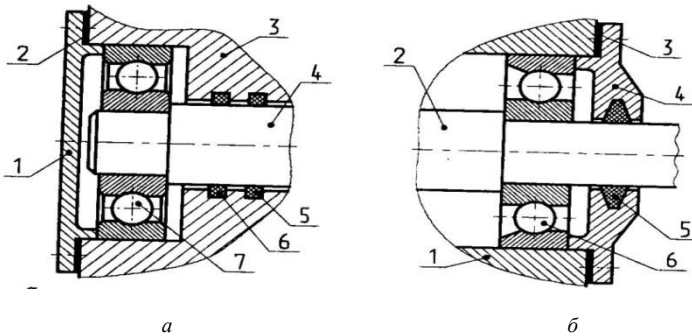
Уплотнители: а – уплотнители крышки, корпуса и вала; 1 – крышка; 2 – прокладка; 3 – корпус; 4 – вал; 5, 6 – резиновые кольца; 7 – подшипник; б – уплотнители корпуса, вала и крышки; 1 – корпус; 2 – вал; 3 – прокладка; 4 – крышка; 5 – кольцо войлочное; 6 – подшипник
